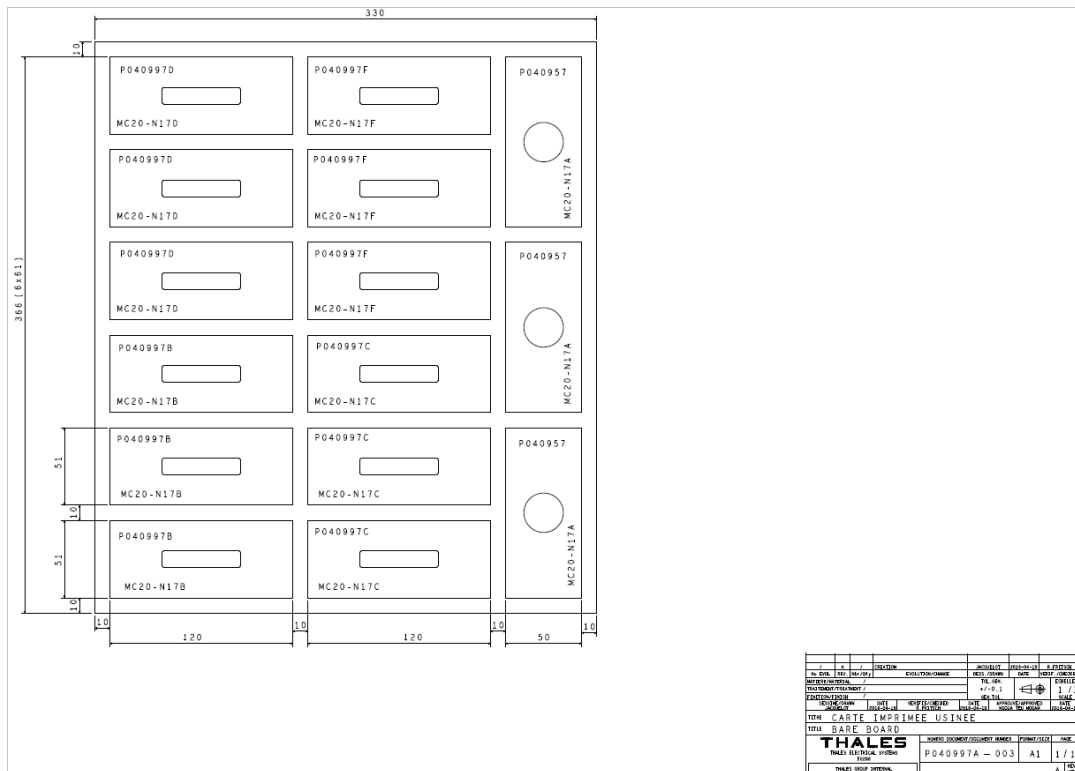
Mise en panneau des prototypes de planar PCB
